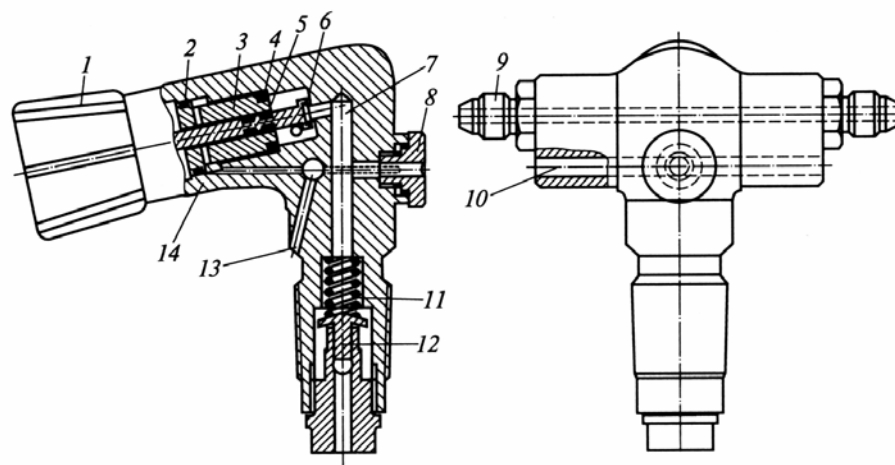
Вентиль баллонный для дренажной схемы подключения:
